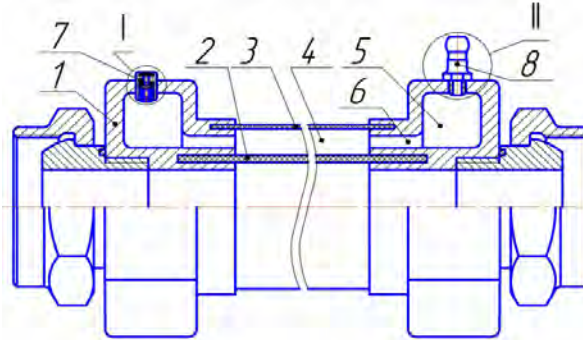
Трубопровод высокого давления: 1 — наконечник; 2 — силовой рукав; 3 — оболочка; 4 — полость; 5 — камера; 6 — кольцевой канал; 7 — редукционный клапан; 8 — обратный клапан
